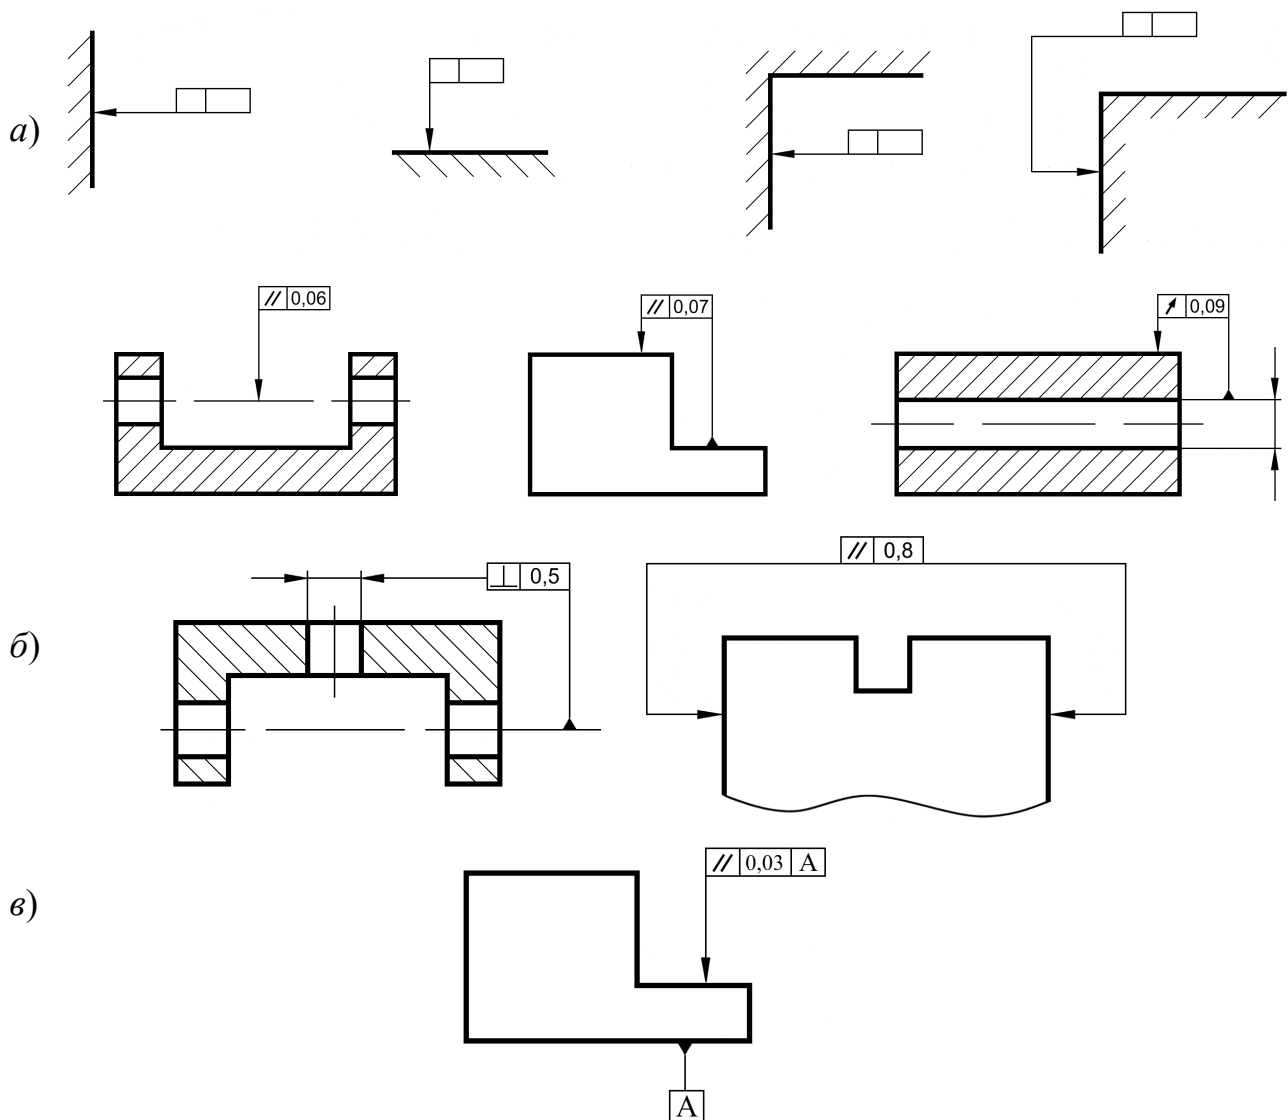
Примеры условных обозначений допусков формы и расположения поверхностей
